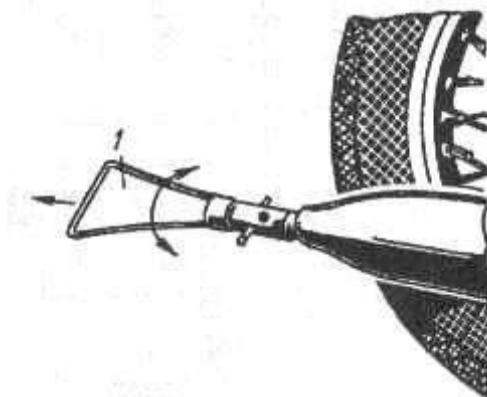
Извлечение трубы акустического фильтра из корпуса глушителя шума выпуска
